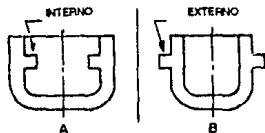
Entalladuras externa e interna. (Ref. 2).
